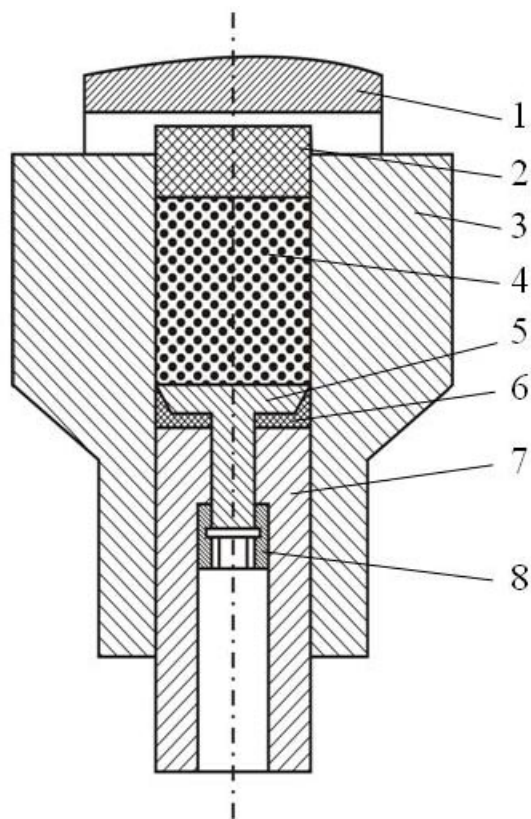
Прессформа для брикетирования исходной шихты: 1 – опорная крышка; 2 – пористый вкладыш; 3 – корпус; 4 – брикет исходной шихты; 5 – поршень; 6 – манжета; 7 – шток; 8 – гайка
